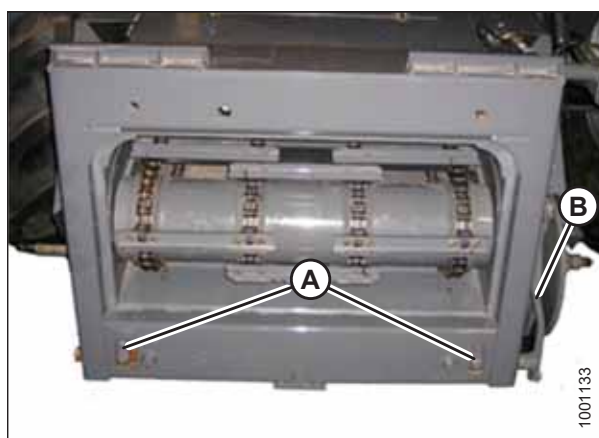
Hydraulická a elektrická sružená spojka
